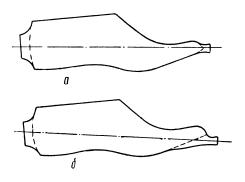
Способы закрепления исходной модели в копировально-фрезерном станке: штрих-пунктирная линия — ось закрепления модели в станке; пунктирная линия — контур готовой колодки
